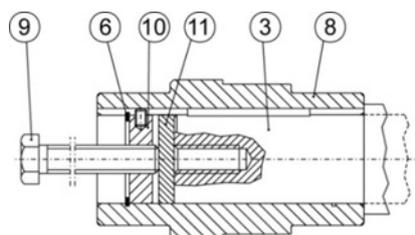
Desmontaje del eje del cliente con o sin el tope de contacto
